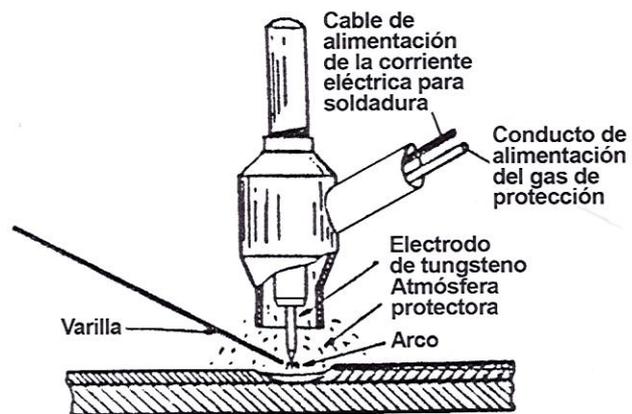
| Electrodo, pileta líquida y metal de soldadura en proceso TIG
